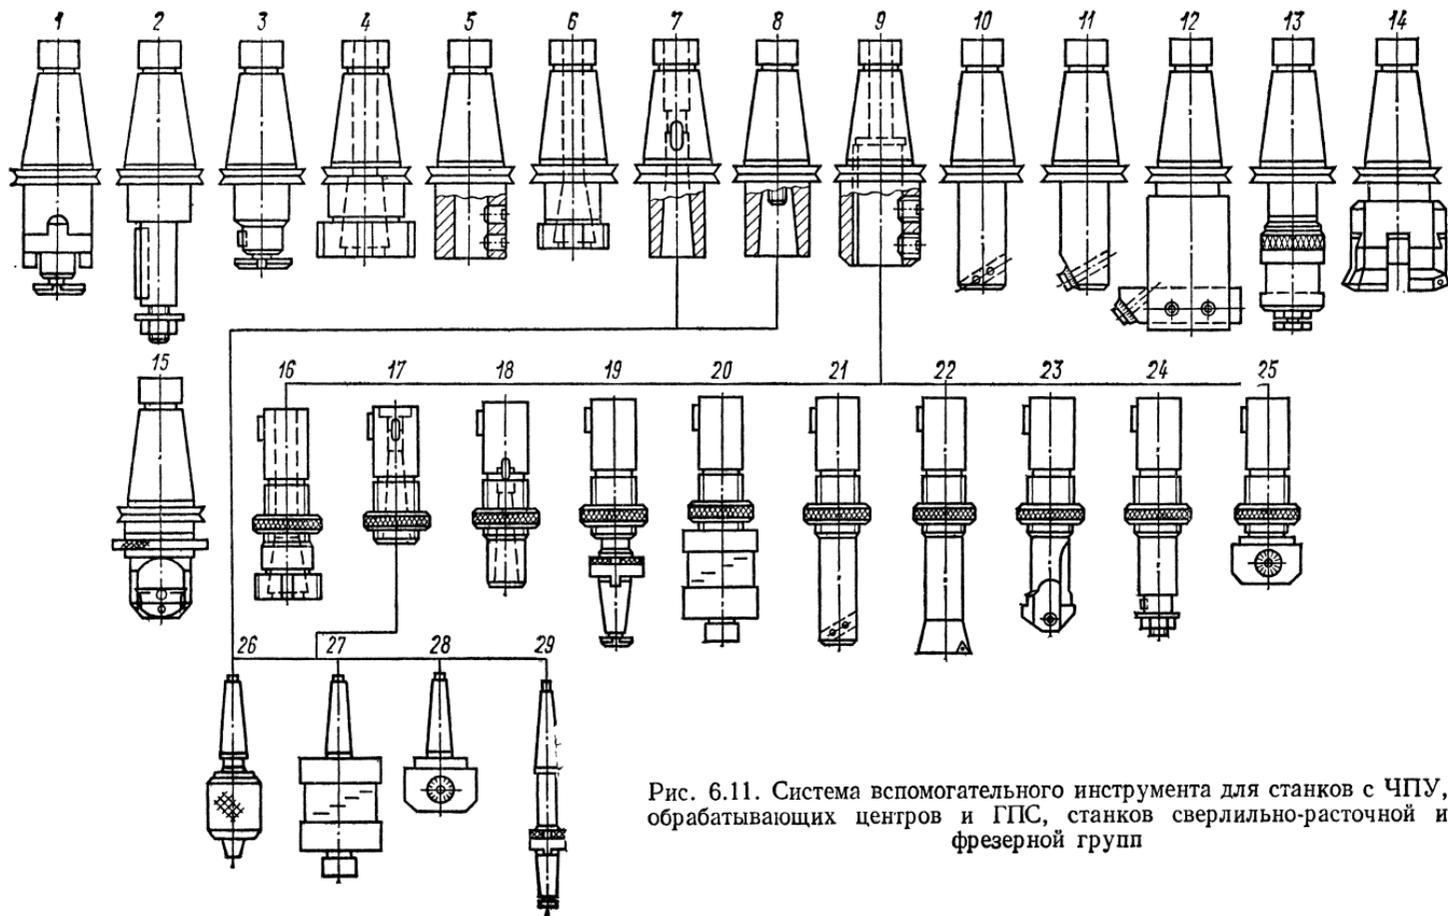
Система вспомогательного инструмента для станков с ЧПУ, обрабатывающих центров и ГПС, станков сверлильно-расточной и фрезерной групп
